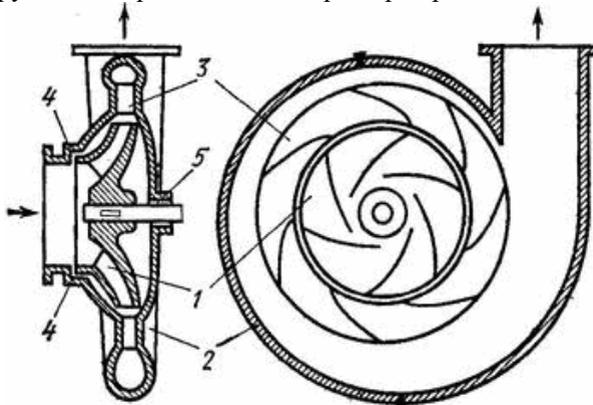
Конструкция центробежного компрессора: 1- рабочее колесо; 2- корпус; 3- отвод (лопаточный диффузор); 4- подвод (входное устройство); 5- вал
